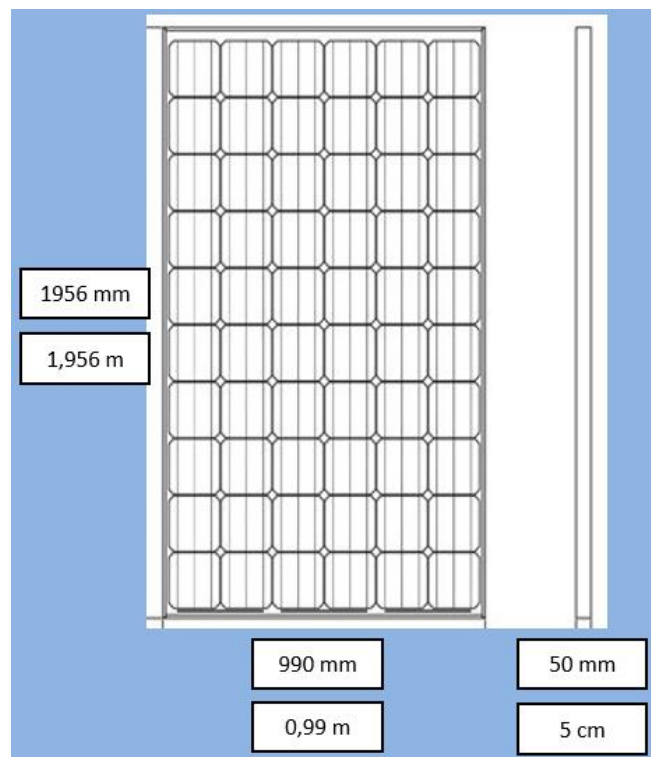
Dimensiones del panel fotovoltaico CSUN/CSUN 320-72P. [26]
